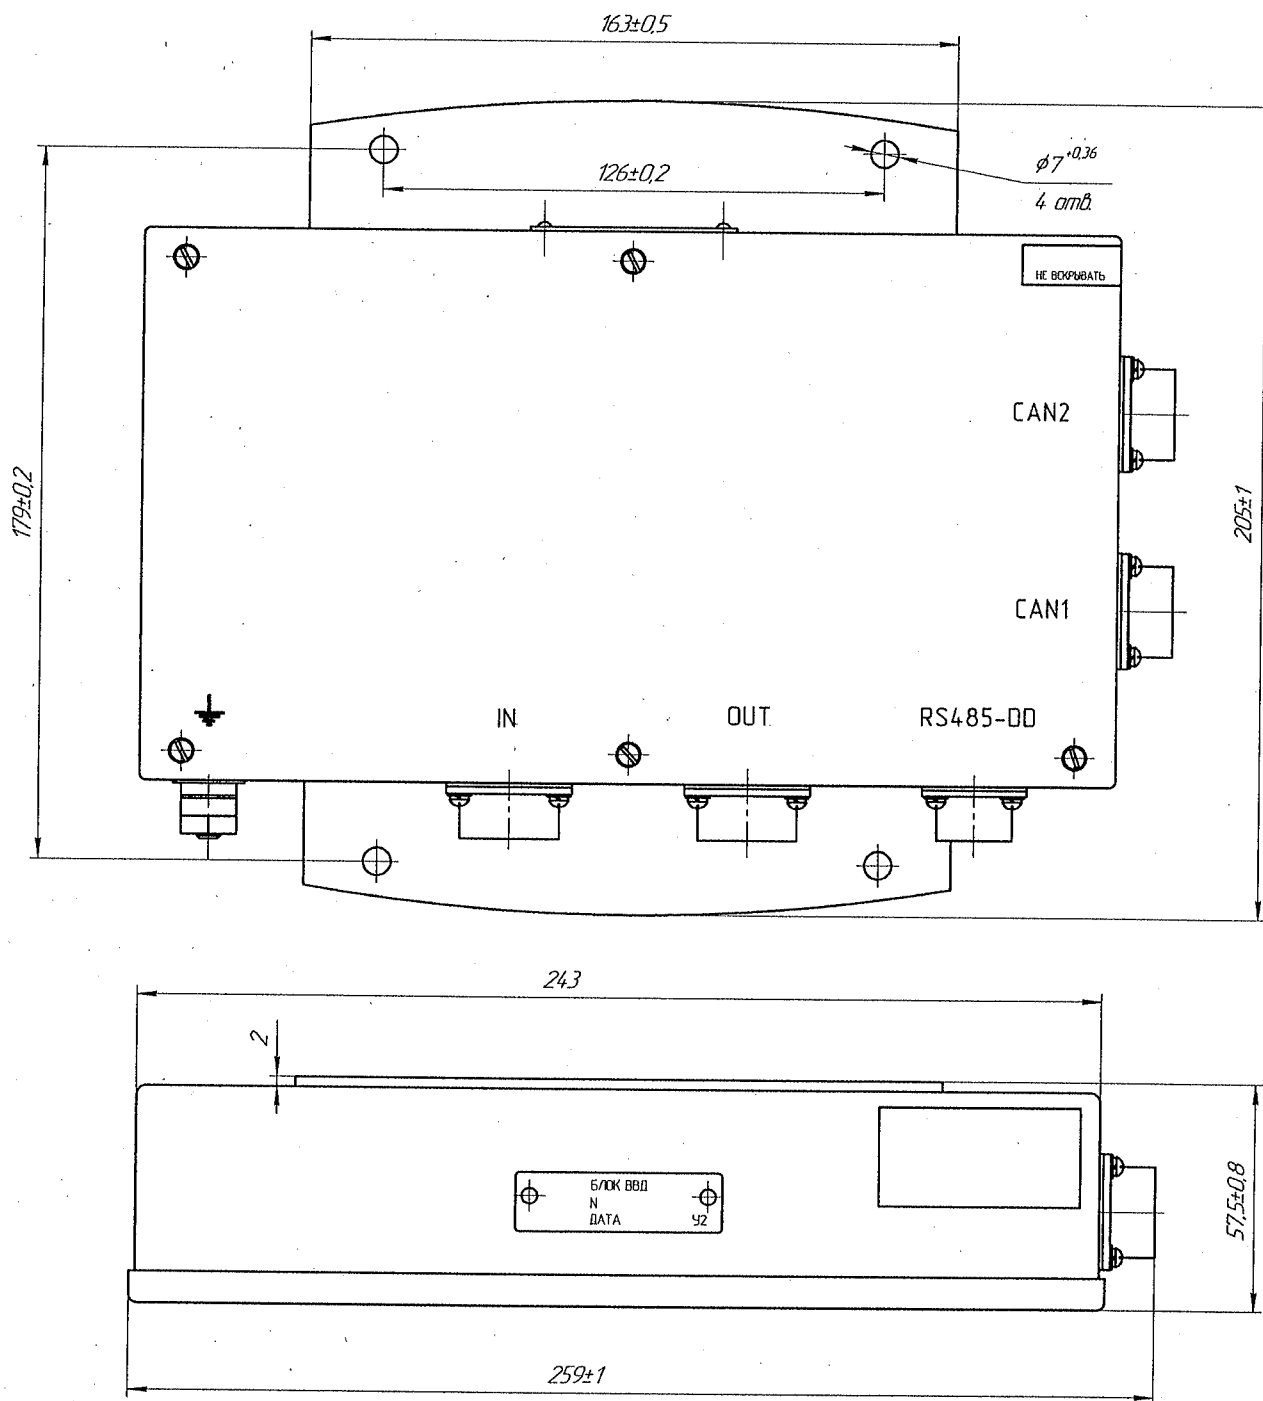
Внешний вид блока ВВД 36311-40-00
